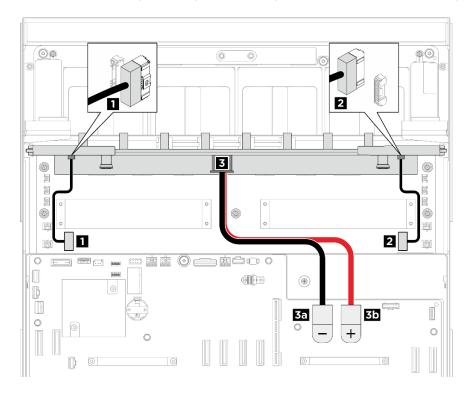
Disposición de los cables de la tarjeta de interposición de PSU
